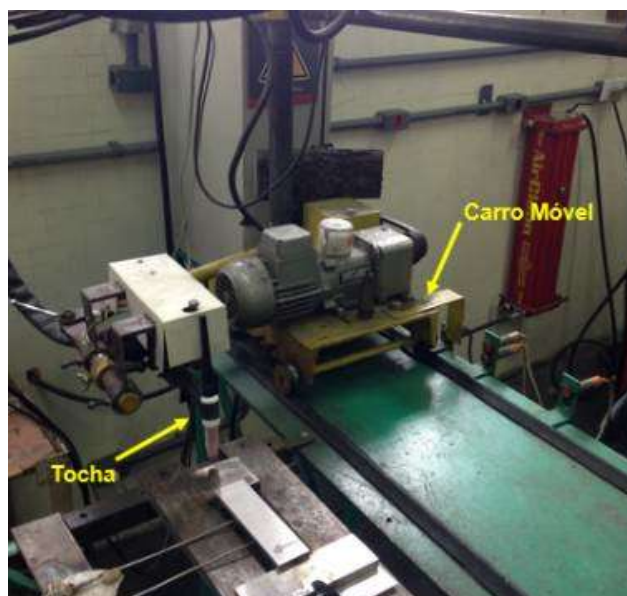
Tocha de soldagem TIG acoplada ao carro móvel.
